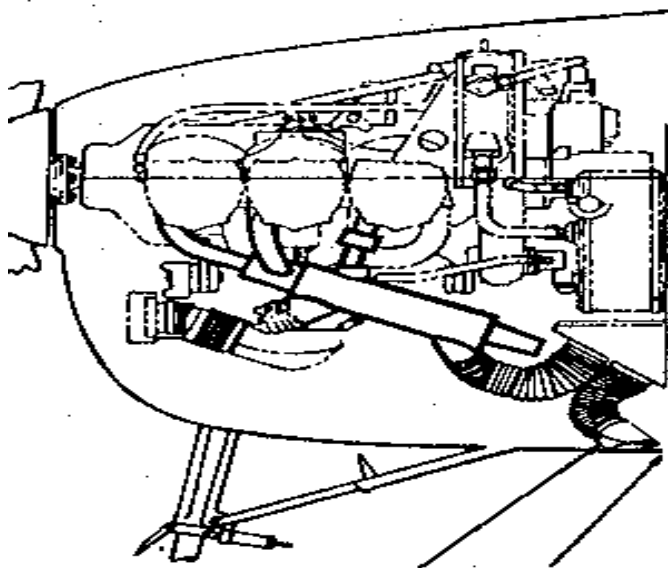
Sistema de escapamento de um motor de cilindros horizontalmente opostos.
